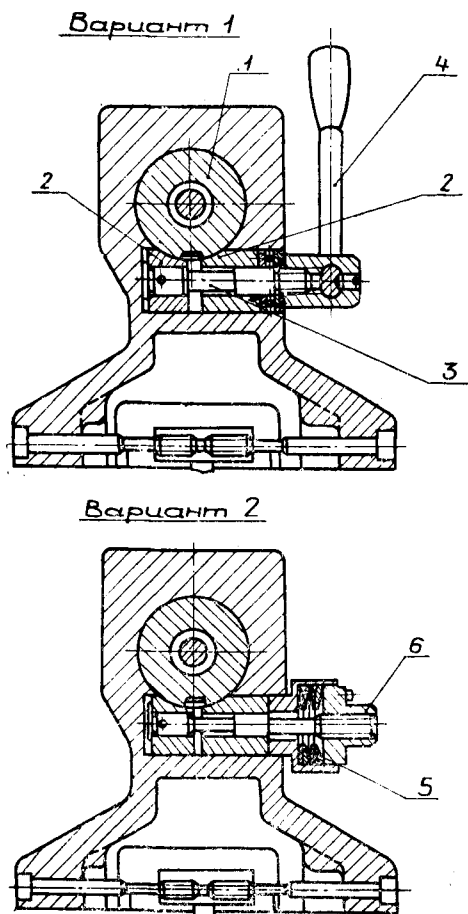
Регулировка радиального подшипника пиноли задней бабки
